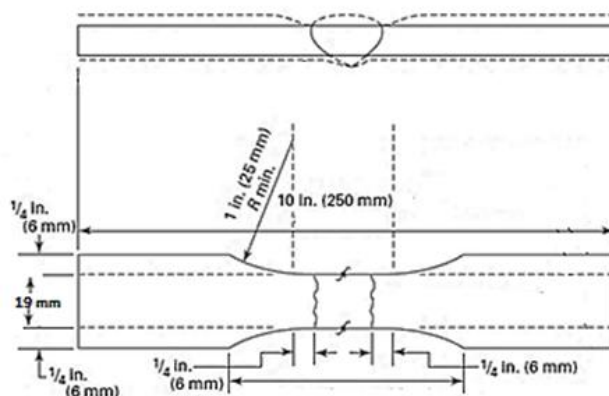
Esquema com a dimensão do corpo de prova de tração transversal das soldas de acordo com a norma ASME BPVC Section IX: 2010, QW-462.1 (b) [9].
